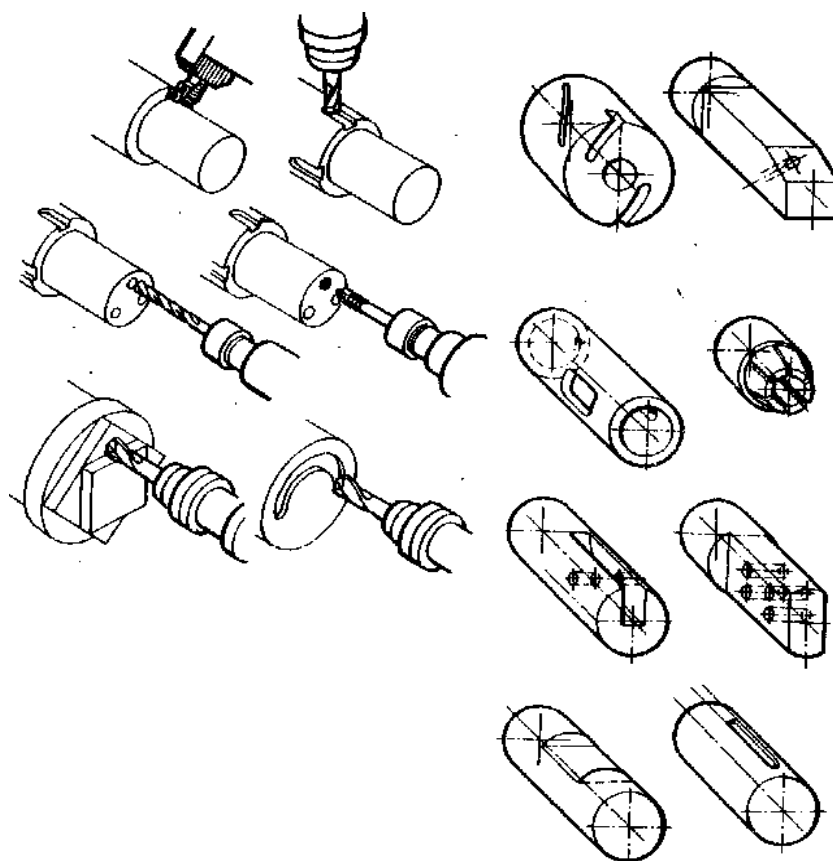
Примеры обработки на станках с револьверной головкой с приводными шпинделями
